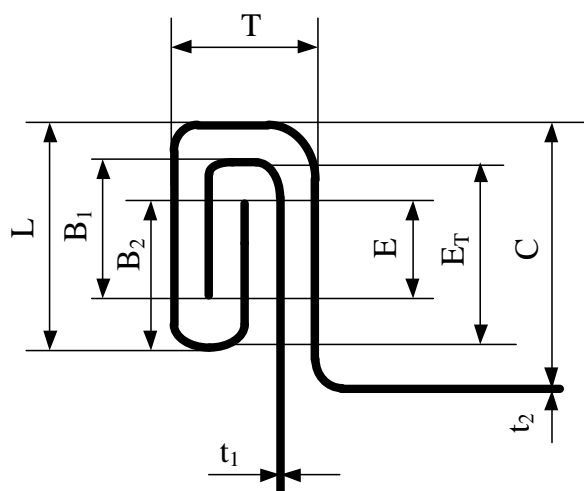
Схема двойного закаточного шва:  $t_1$  – толщина материала банки;  $t_2$  – толщина материалы крышки;  $L$  – ширина закаточного шва;  $C$  – глубина посадки крышки;  $B_1$  – ширина крючка банки;  $B_2$  – ширина крючка крышки;  $T$  – толщина закаточного шва;  $E$  – ширина перекрытия закаточного шва;  $E_T$  – теоретическая ширина перекрытия закаточного шва.
